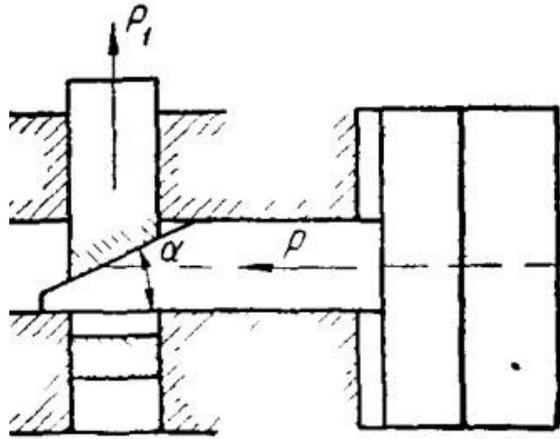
Схема клинового механизма с передачей движения под углом 90° .
